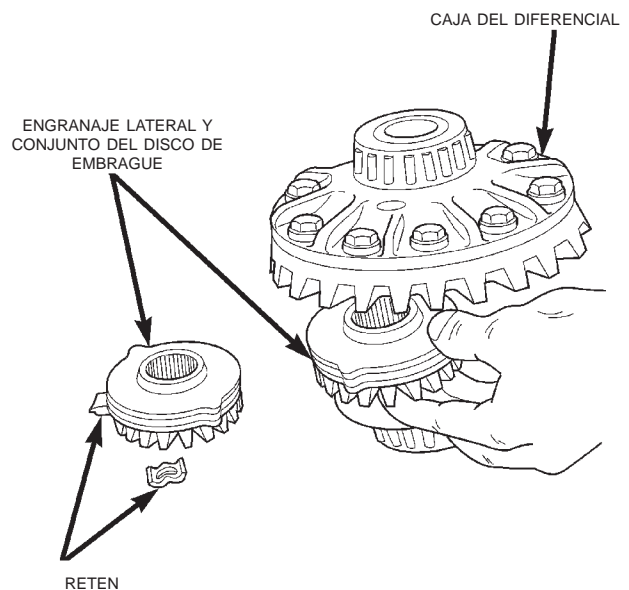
Desmontaje del engranaje lateral y el disco de embrague
